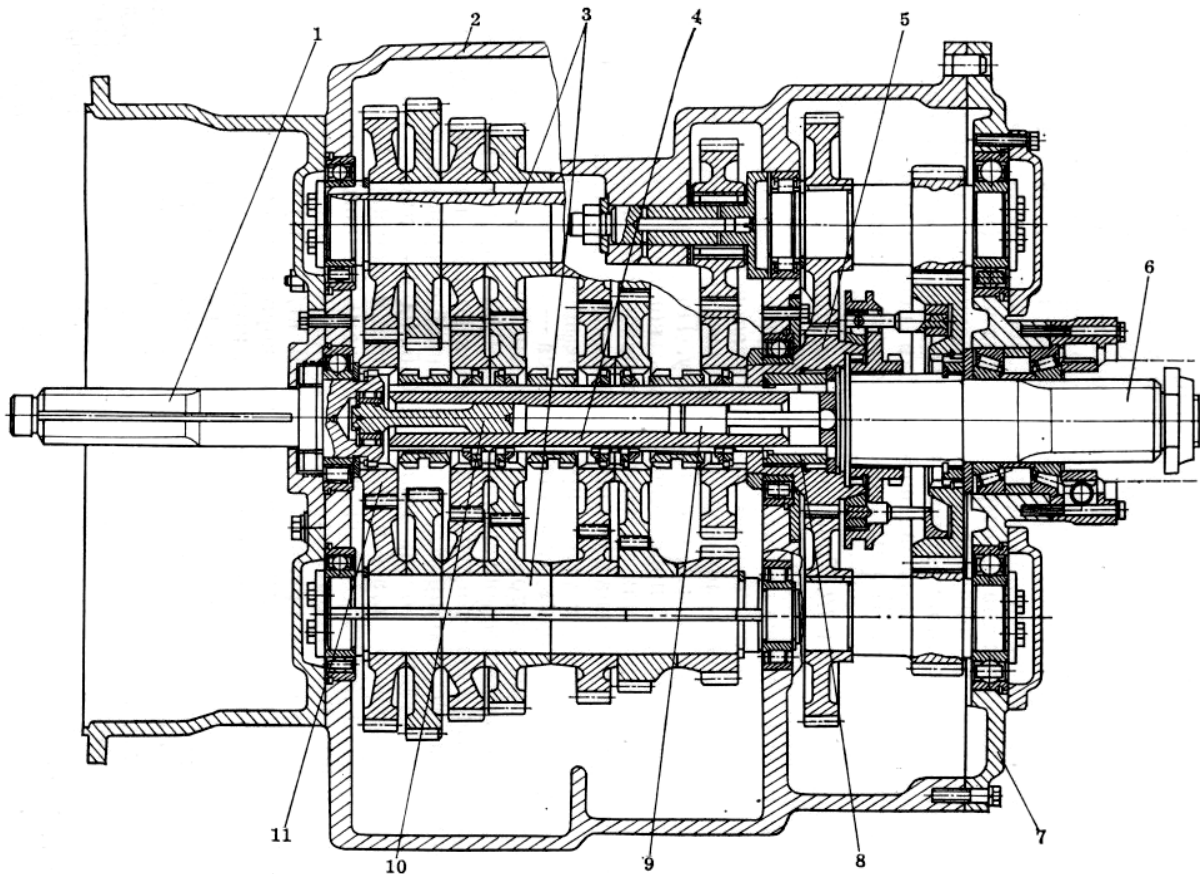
Конструкция десятиступенчатой коробки передач
